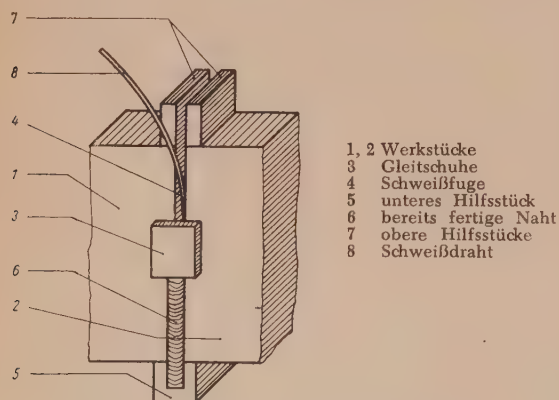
Prinzip des Elektro-Schlacke-Schweißens
